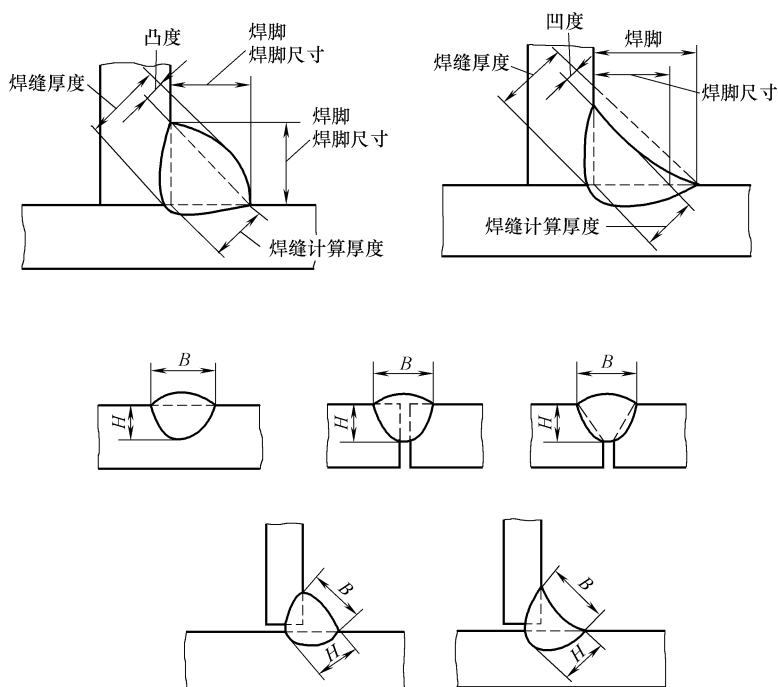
焊缝计算厚度和焊缝宽度
